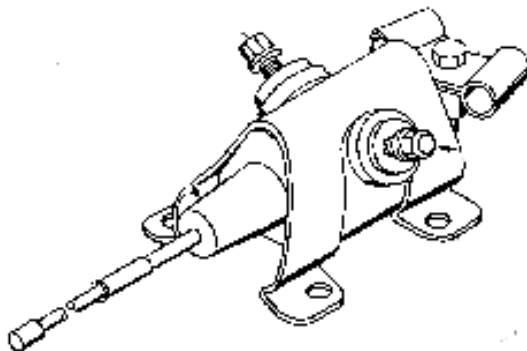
Внешний вид датчика пожара/перегрева силовой установки
